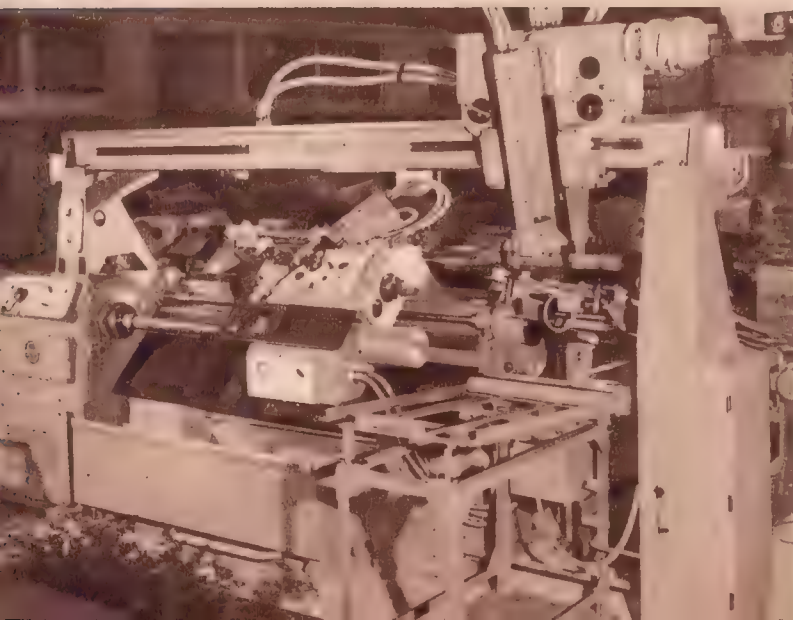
Die bekannte Magdeburger automatische Hartmetallkopierdrehmaschine „Magkomat“ ist mit einer Führungssteuerung zum Kopieren der Modellwelle ausgestattet. Unser Bild zeigt die nach dem Baukastenprinzip konstruierte Maschine mit selbsttätiger Werkstückzuführung.
